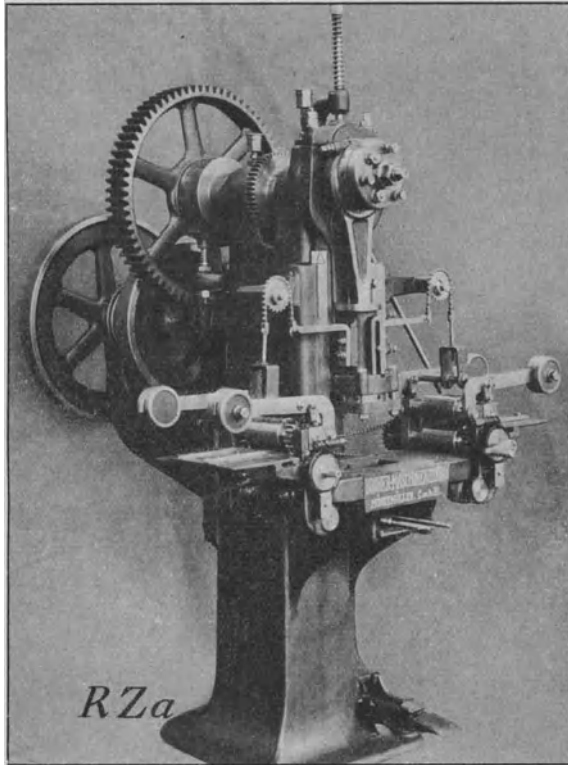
Bonner Maschinenfabrik Mönkemöller & Co.
